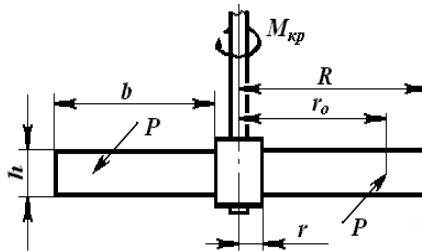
Розрахункова схема лопатевої мішалки
